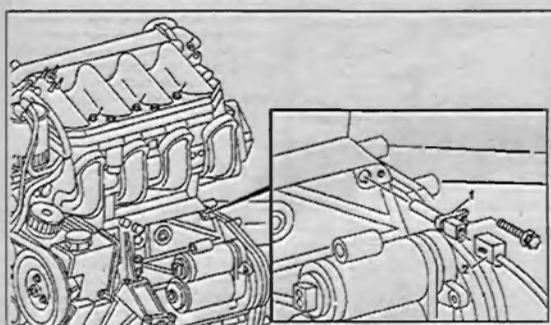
Снятие и установка датчика положения коленчатого вала:
